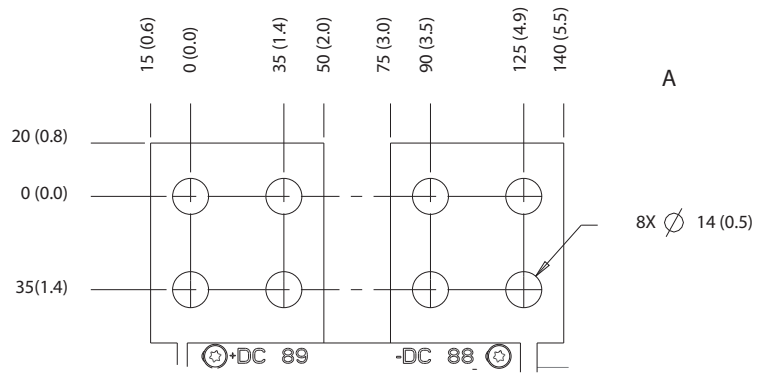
Dimensions des bornes de répartition de la charge/régénératrices E4h
